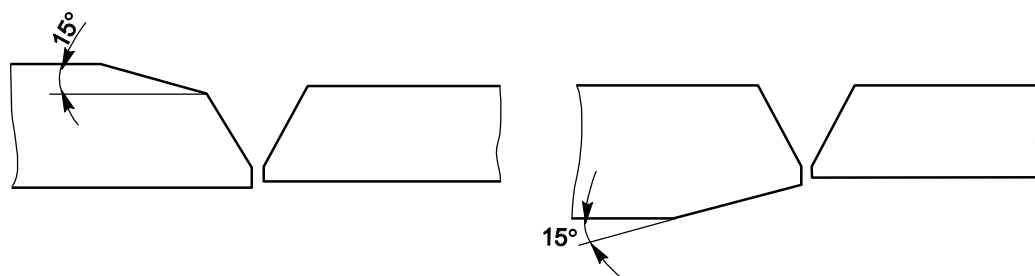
Подготовка стыка из разнотолщинных деталей
